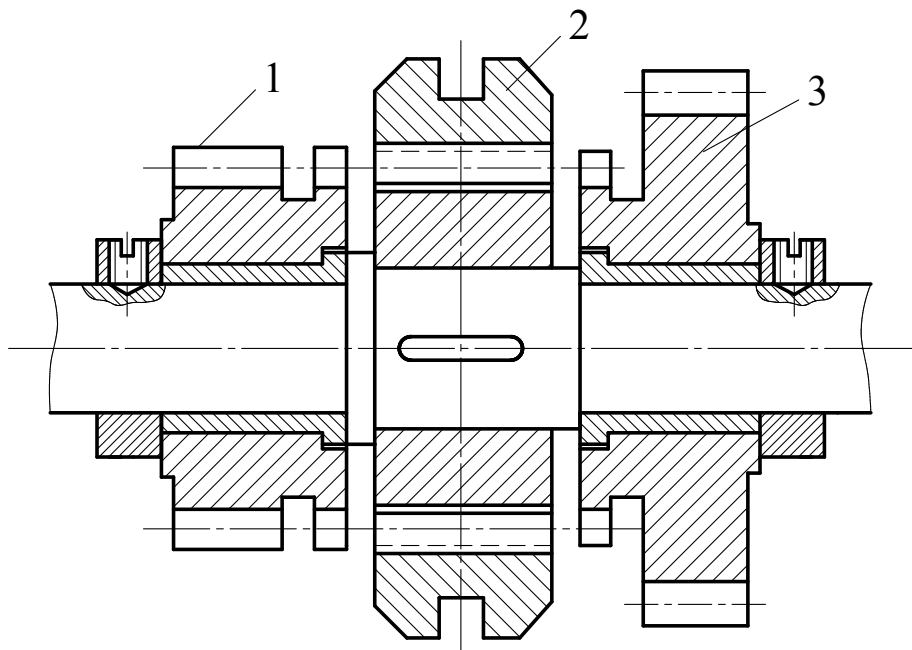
Муфта зубчатая сцепная с внешней обоймой
